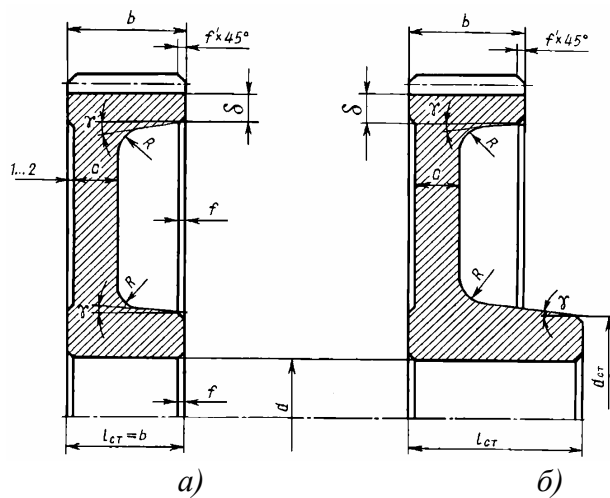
Конструкции штампованных цилиндрических зубчатых колес при односторонней штамповке
